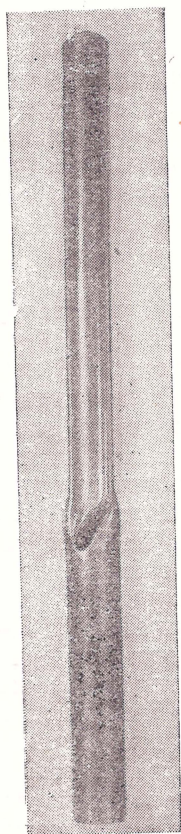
Заготовка сверла, обработанная на вальцековочной машине
